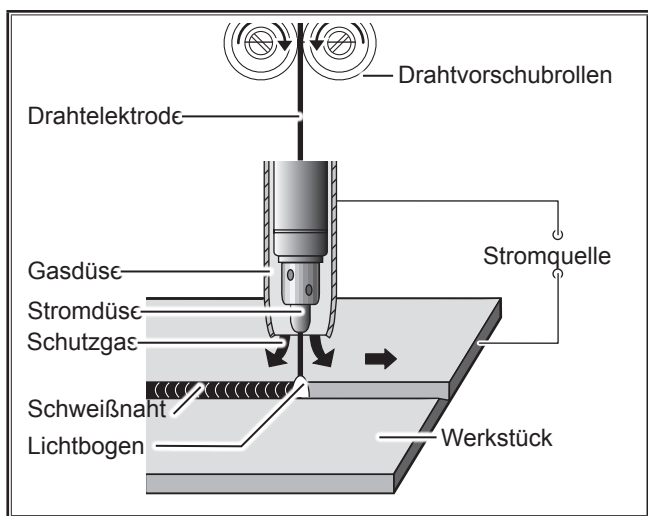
MIG/MAG-Schweißverfahrens
